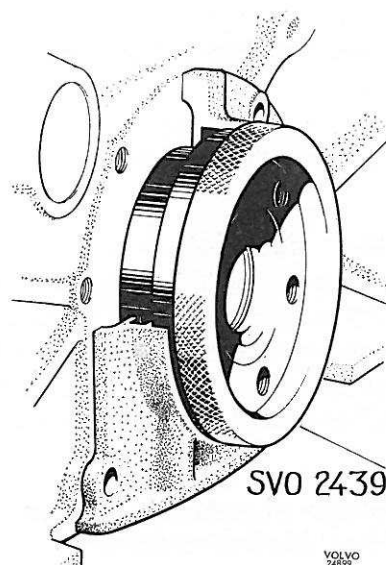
Centrage de la bride d'étanchéité arrière (avec joint de feutre)
